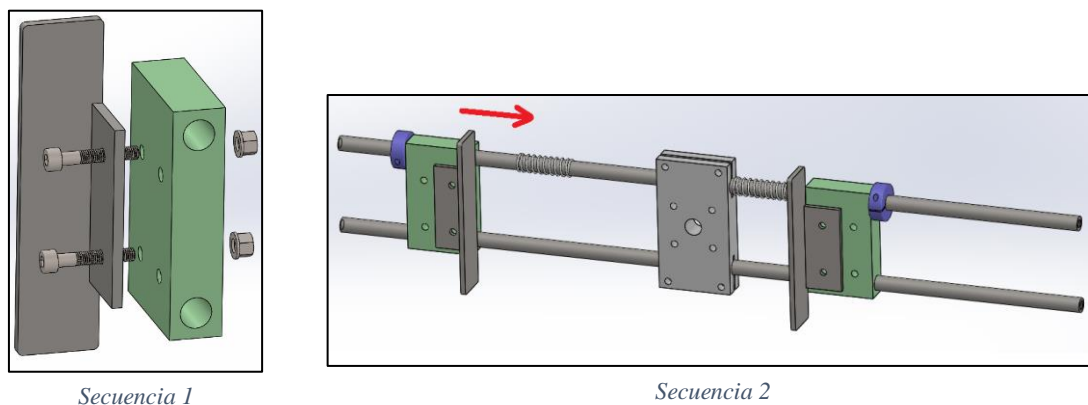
Montaje grupo de piezas apoyo (SS)
